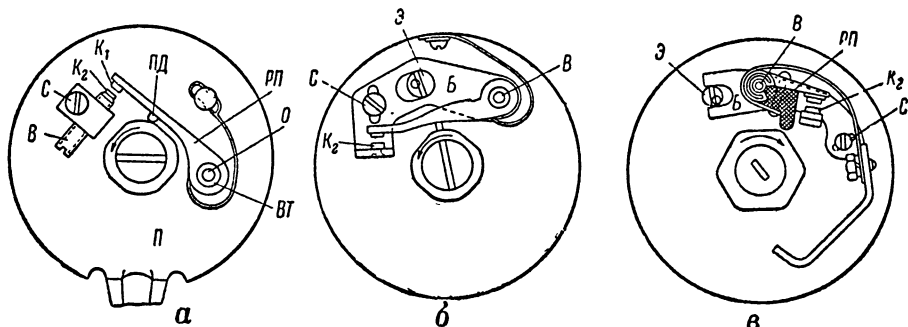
Конструкция типовых прерывателей батарейного зажигания
